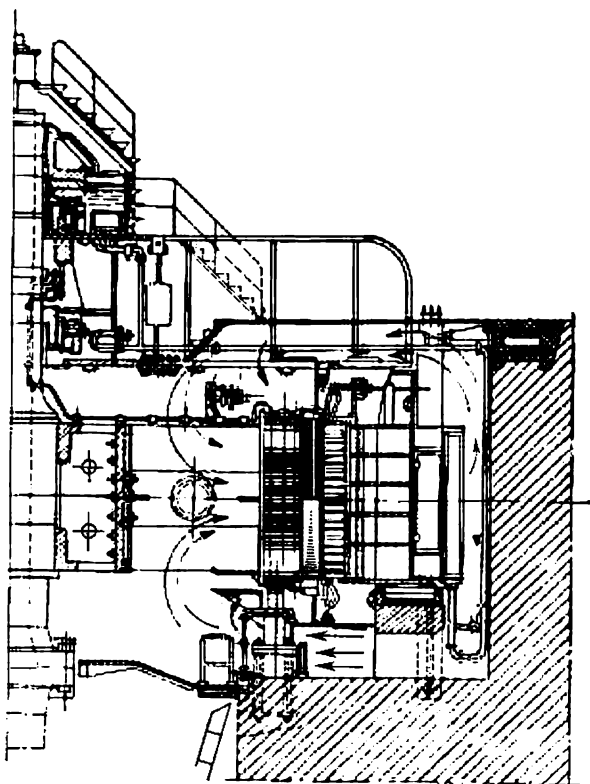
Coupe longitudinale d'un alternateur hydraulique de 225 MW, 125 tr/mn à refroidissement par l'air installé dans la centrale de Bratsk (U.R.S.S.).
